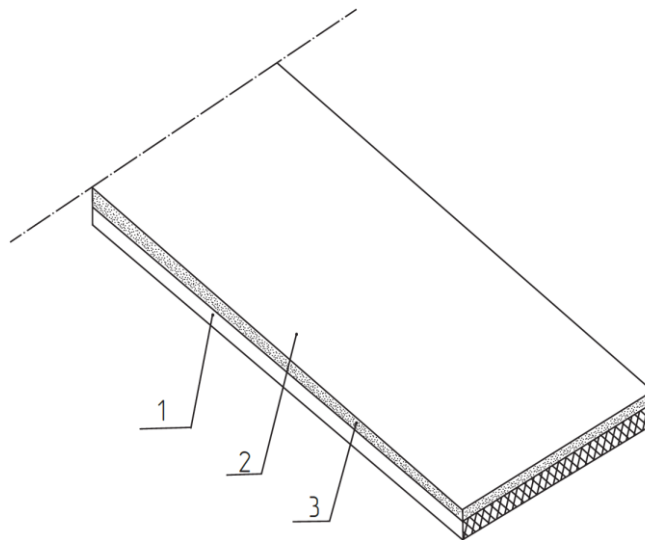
Алмазна стрічка для полірування поверхонь деталей тертя
